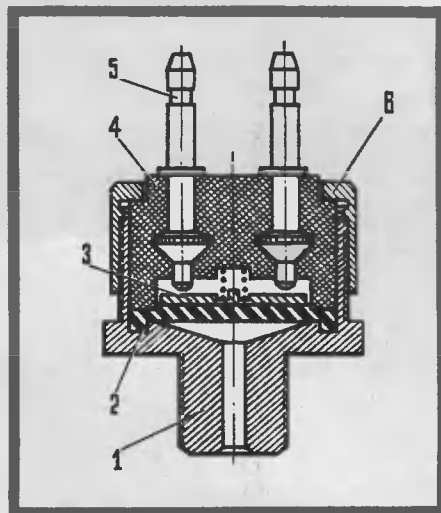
Выключатель в сборе: 1 — корпус; 2 — диафрагма; 3 — контактный диск; 4 — изолятор; 5 — клеммы; 6 — накидная гайка.
